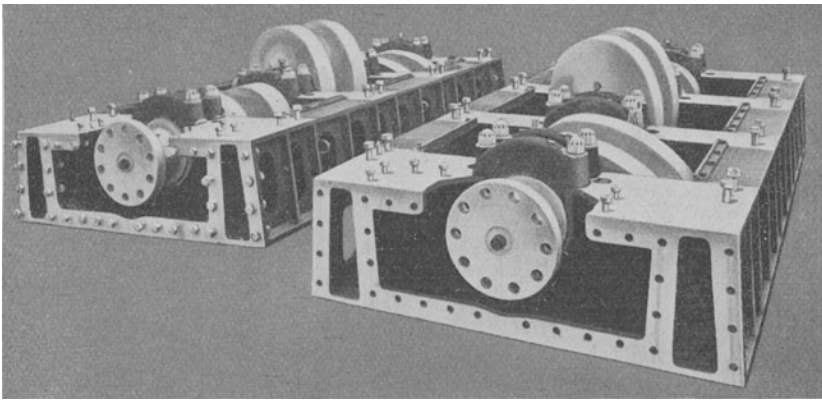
Grundplattenteile einer 6-zylindrigen Ölmaschine.
